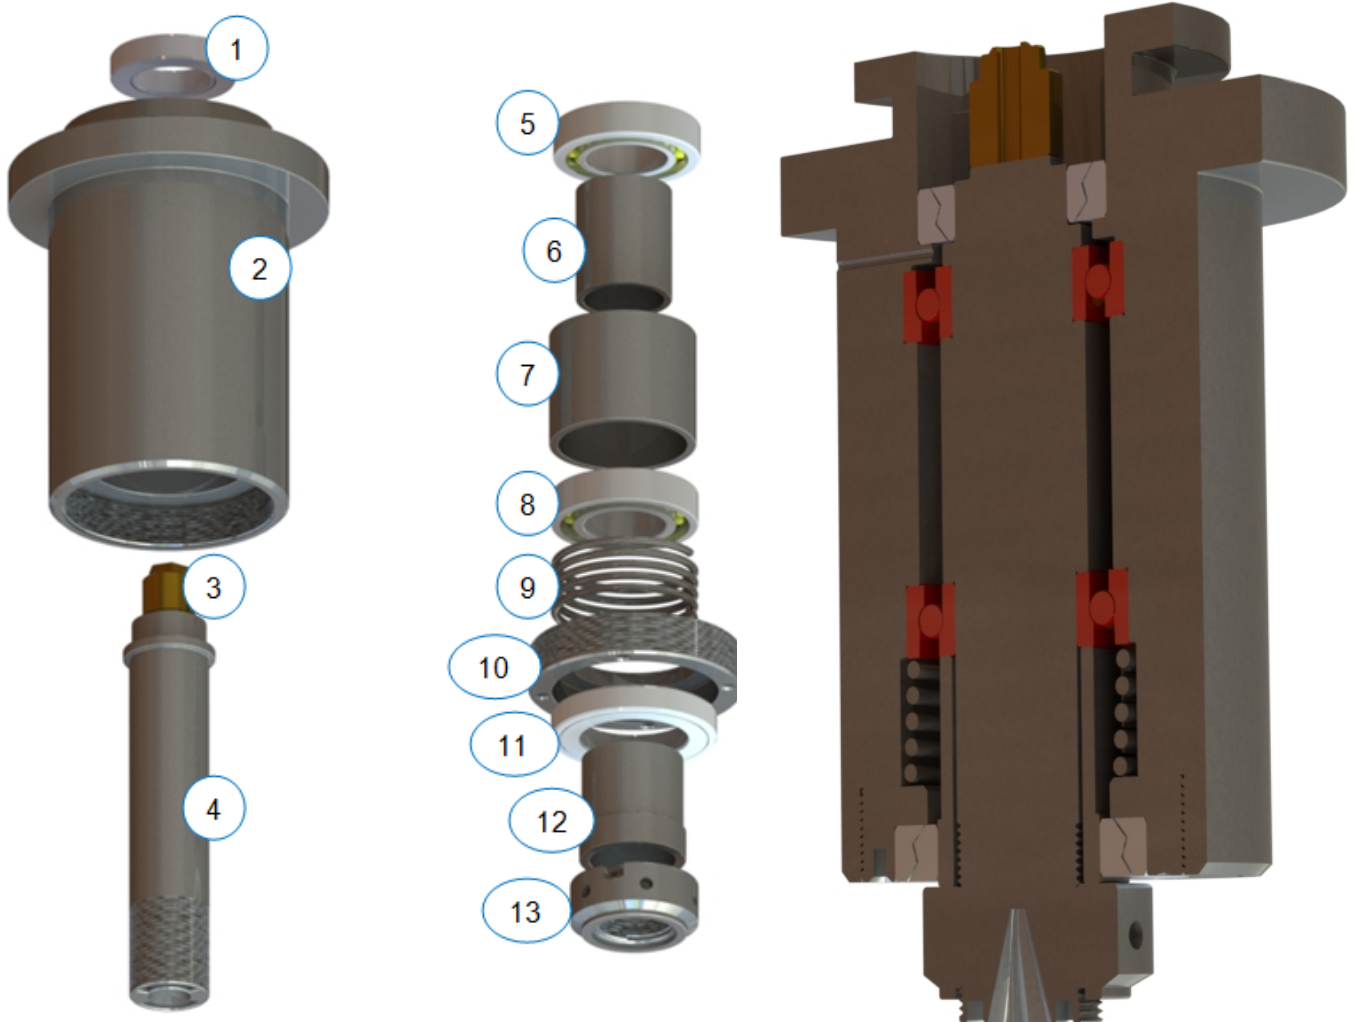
Explosionsdarstellung Werkzeughalter Neuauslegung
